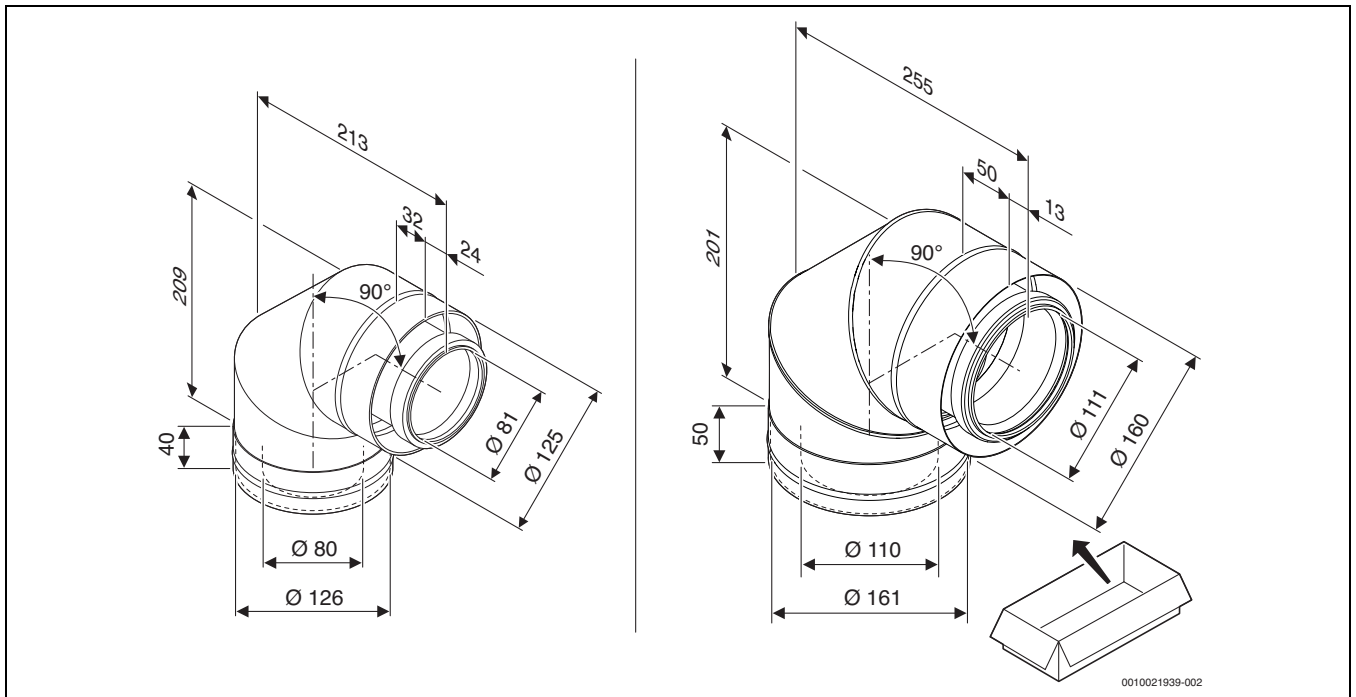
Ø 80/125 mm: 7738112700, Ø 110/160 mm: 7738113146
